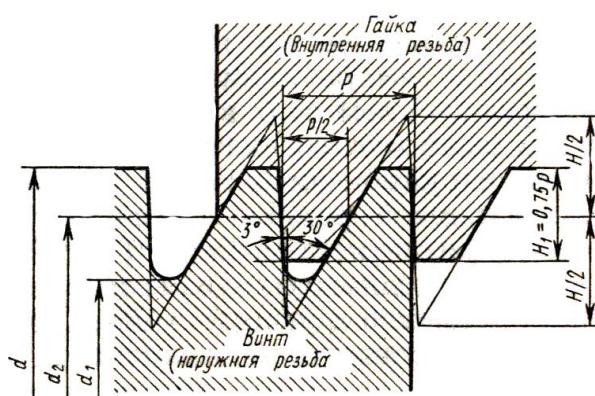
геометрические параметры передачи винт-гайка
